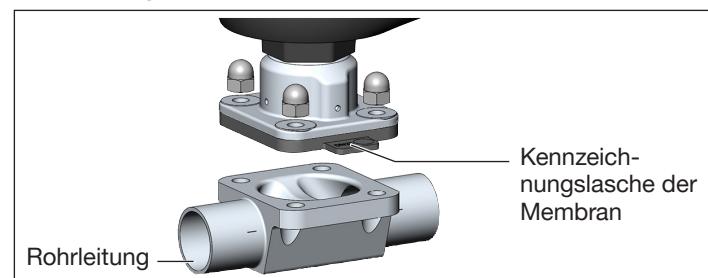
Membran ausrichten (Beispiel 2-Wege-Gehäuse)
